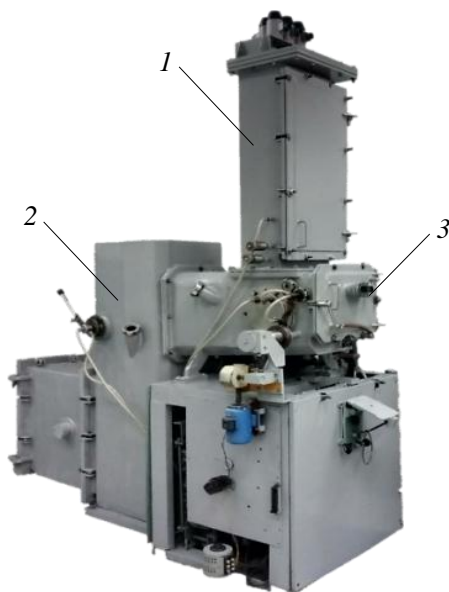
Установка ЭВКР-РН: 1 – питатель; 2 – бункер-приемник готовой продукции; 3 – рабочая камера с системой нагрева
